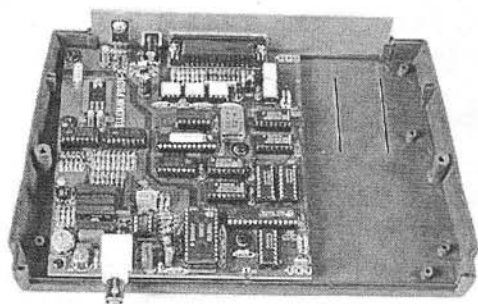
Осциллограф-приставка K8031 в виде конструктора для самостоятельной сборки
